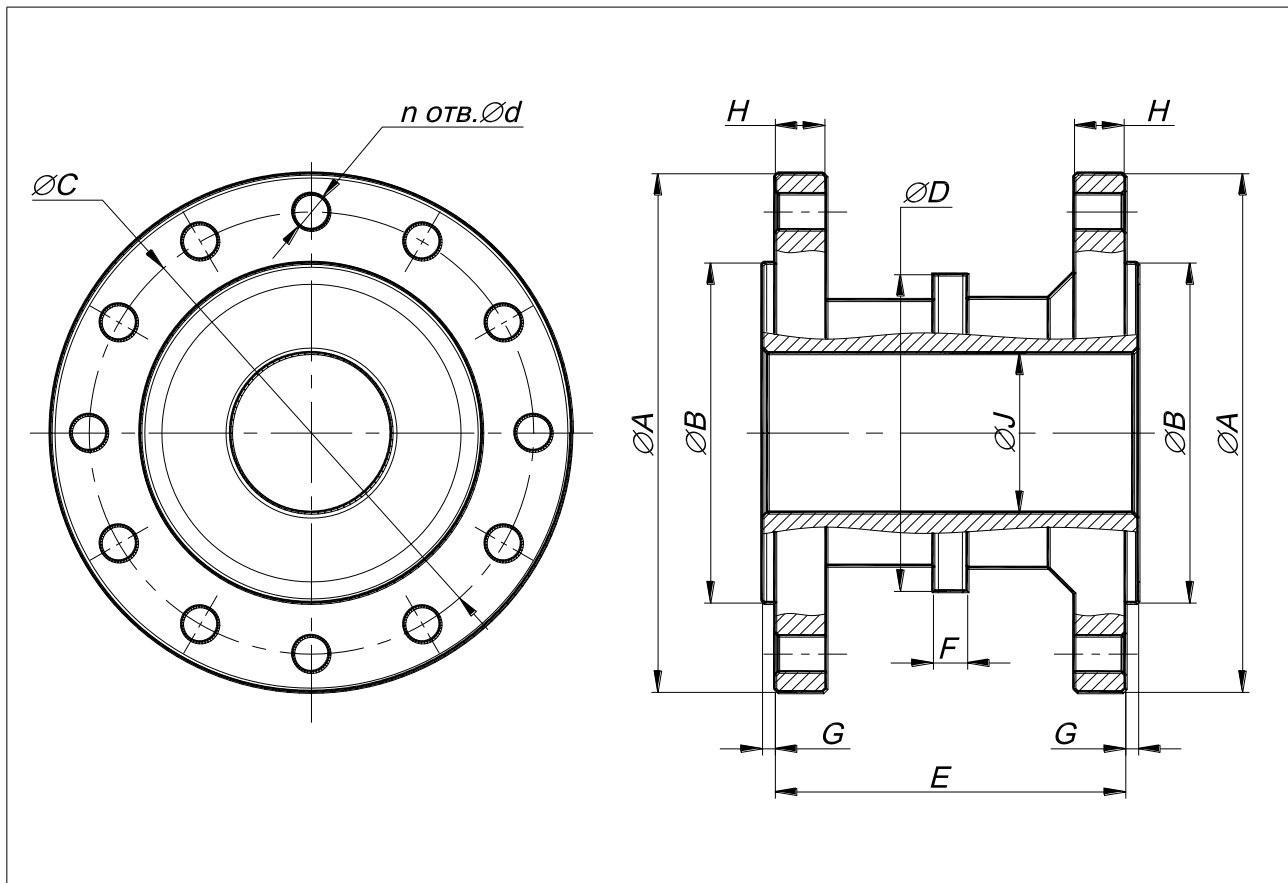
Ротор. Габаритные и установочные размеры, мм.
